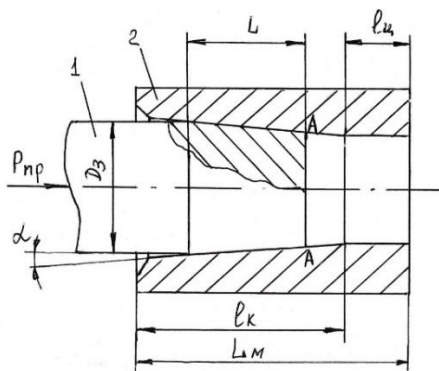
Схема запресування кінця заготовки у матрицю: 1 – заготовка; 2 – матриця
